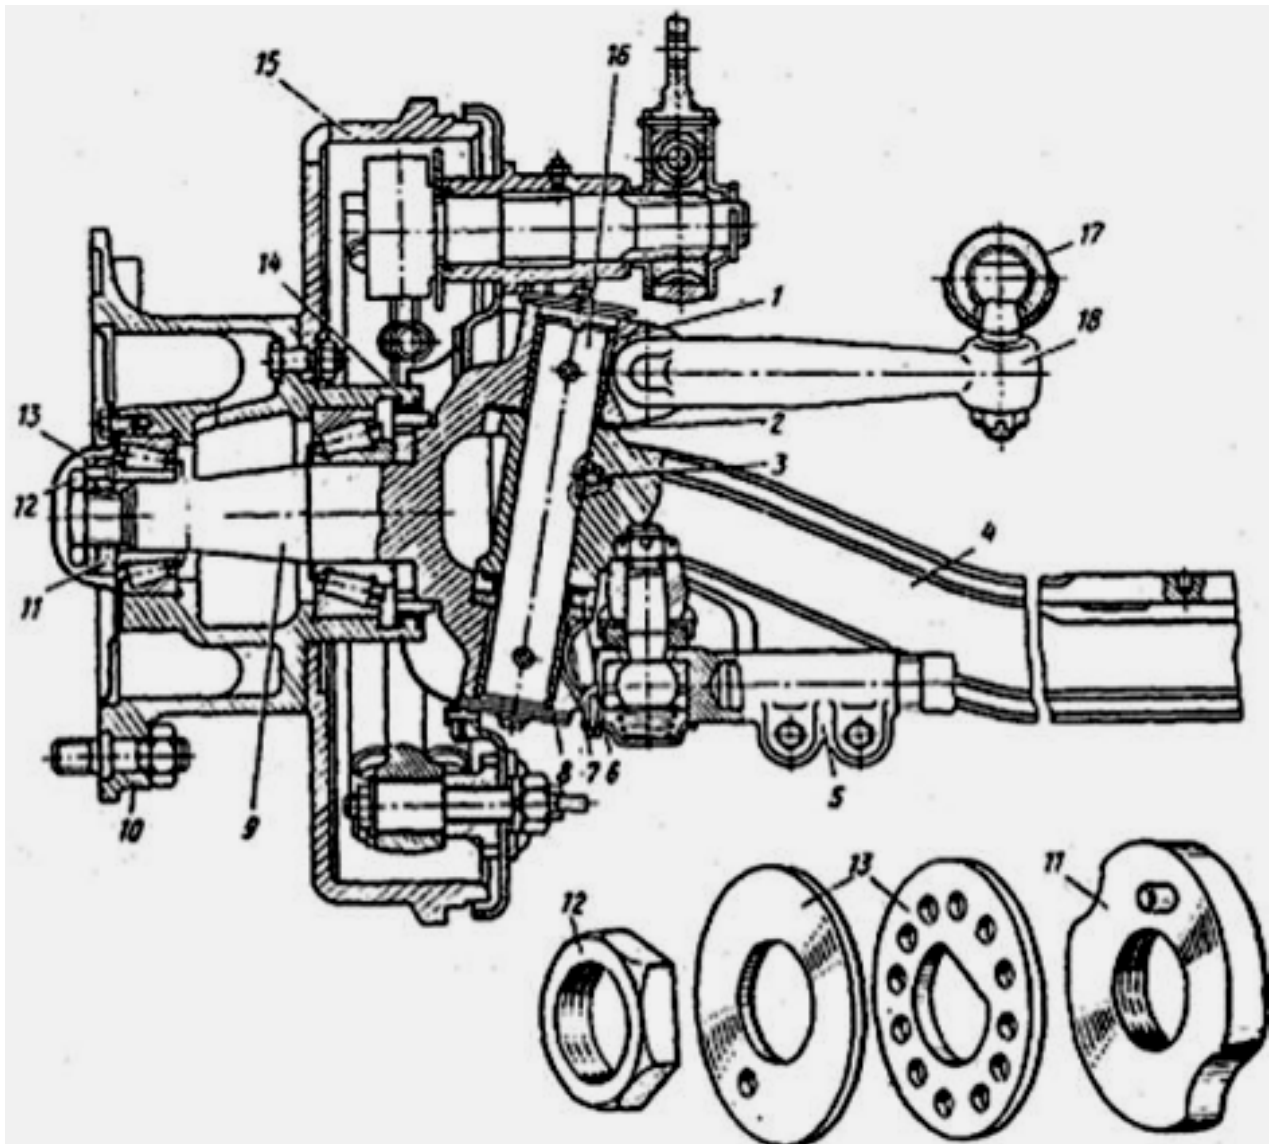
Передний мост грузового автомобиля ЗИЛ-130: 1 и 8 - втулки шкворня; 2 - регулировочные прокладки; 3 - клиновой болт; 4 - балка моста; 5 - поперечная рулевая тяга; 6 и 7 - шайбы опорного подшипника; 9 - поворотная цапфа; 10 - ступица колеса; 11 - регулировочная гайка; 12 - контргайка; 13 - замочная шайба; 14 - сальник; 15 - тормозной барабан; 16 - шкворень; 17 - продольная рулевая тяга; 18 - поворотный рычаг
